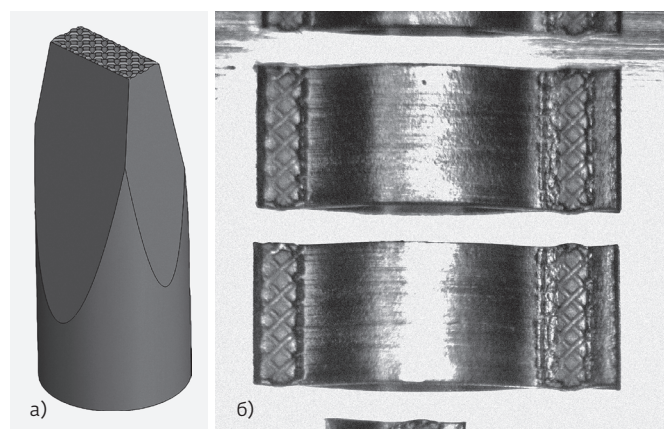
Сварка ленты: а – типовой рабочий торец сварочного инструмента под ленту; б – получаемое соединение
